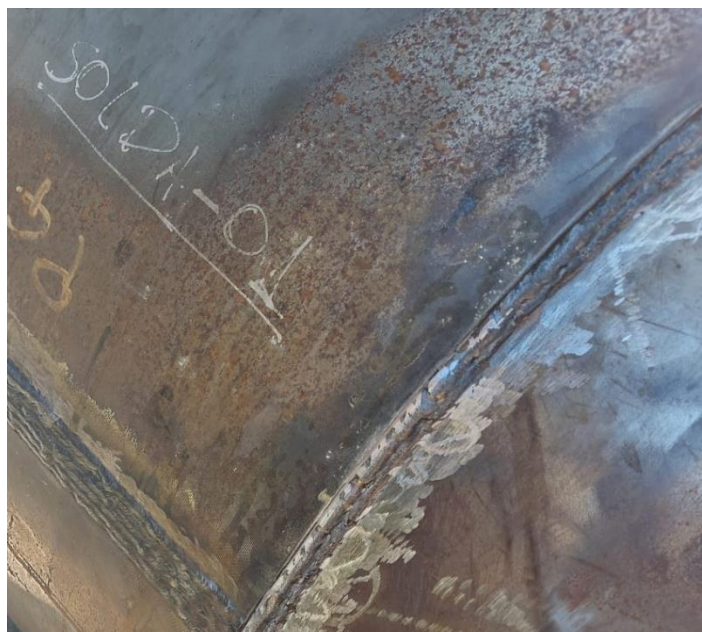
Etapas de pré-aquecimento e soldagem em ângulo.
